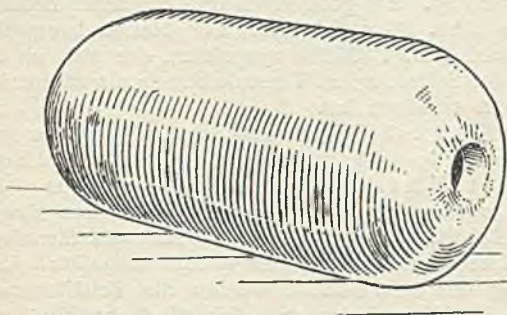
Aus einem Stück geschmiedeter Behälter von Fried. Krupp A. G.
